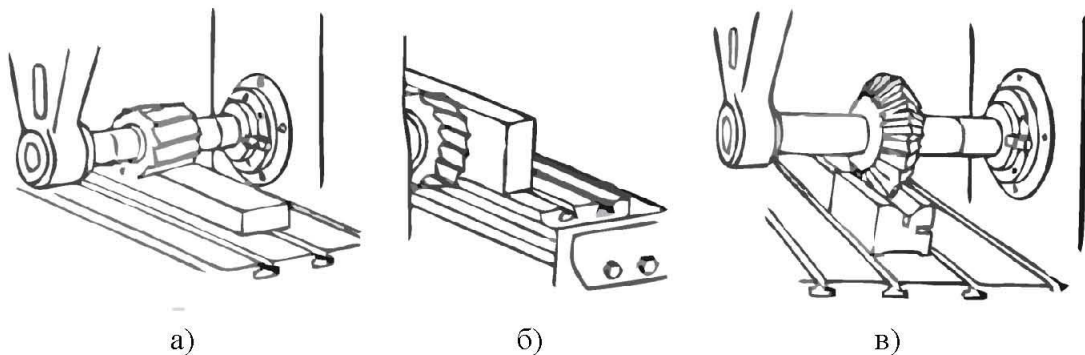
Фрезерування площин: а – циліндричною фрезою, б – торцевою фрезою, в – кутовою фрезою
